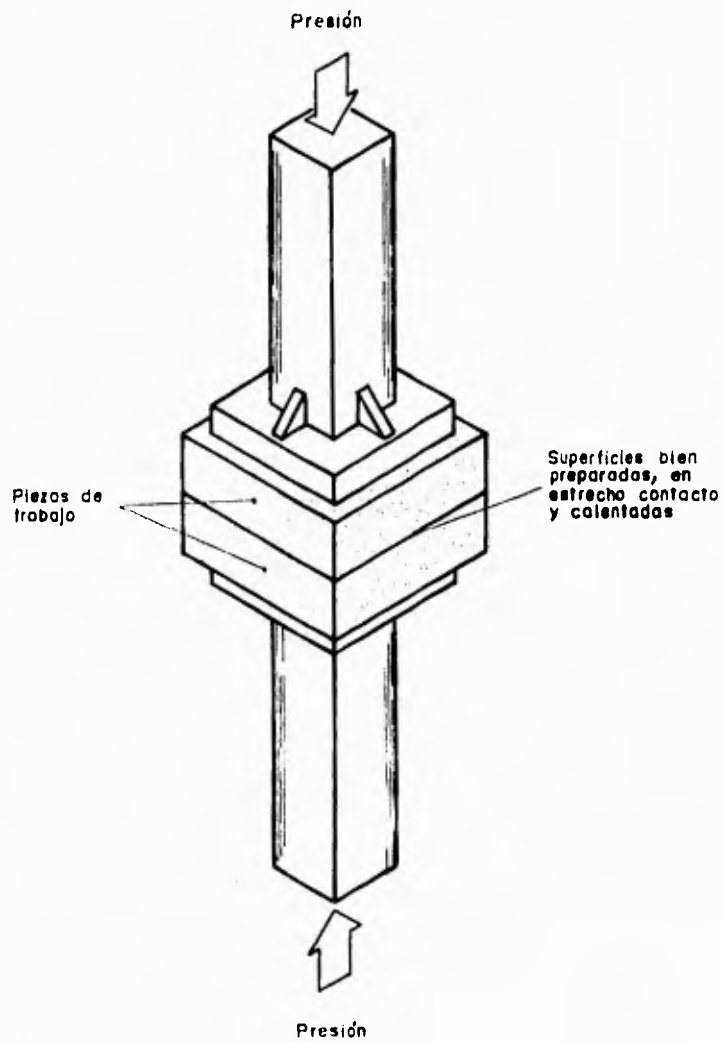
Soldadura por difusión (DFW)
